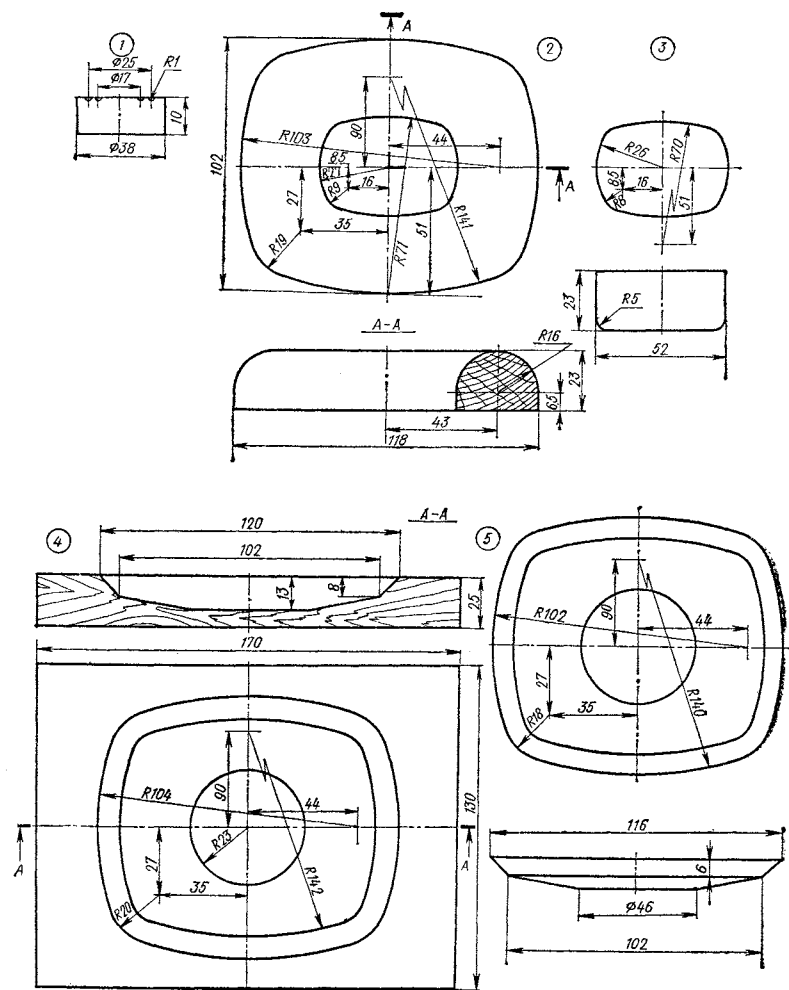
Эскизы приспособления для изготовления телефонов. 1 — матрица для изготовления центрирующей шайбы, текстолит; 2 — модель амбушюра, дерево; 3 — пуансон, дерево; 4 — матрица для штамповки коробки, дерево; 5 — пуансон для штамповки коробки, дерево.
